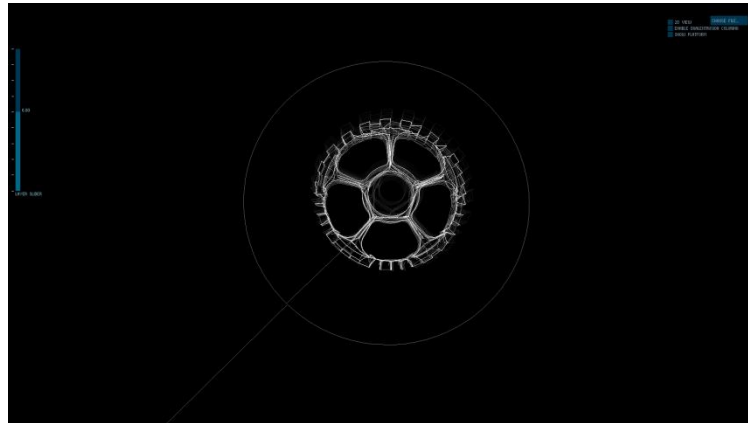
Capa de relleno del Engranaje Configuración #1
